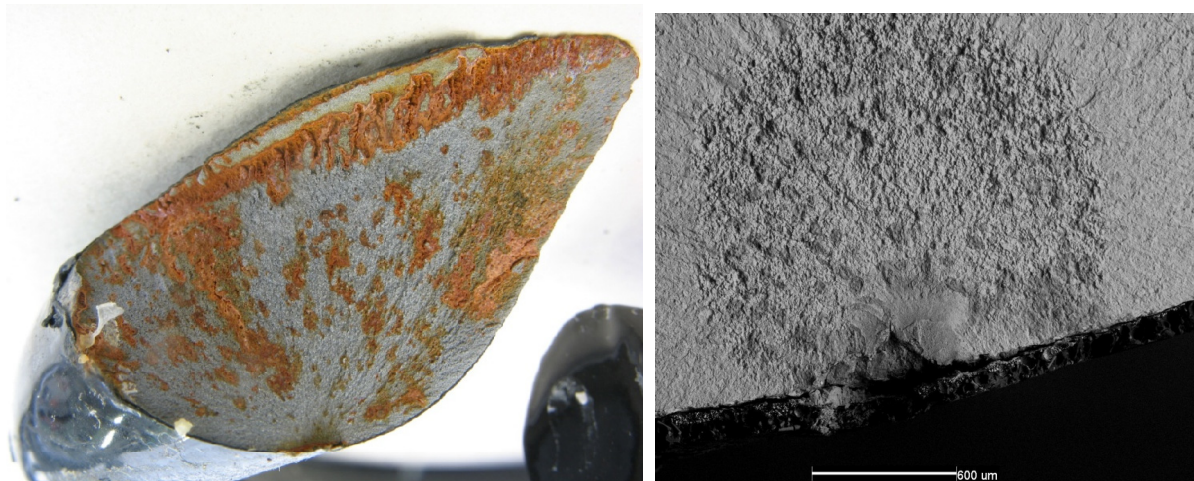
Schwingbruch an Schraubenfeder ausgehend von nichtmetallischem Einschluß
